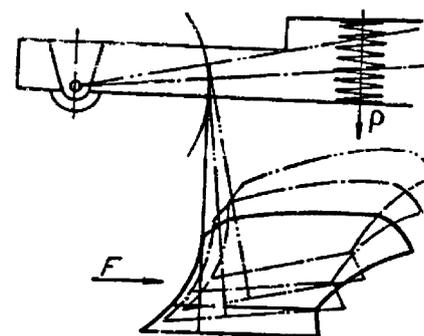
Схема работы плужного корпуса с шарнирно-упругим креплением к раме:
